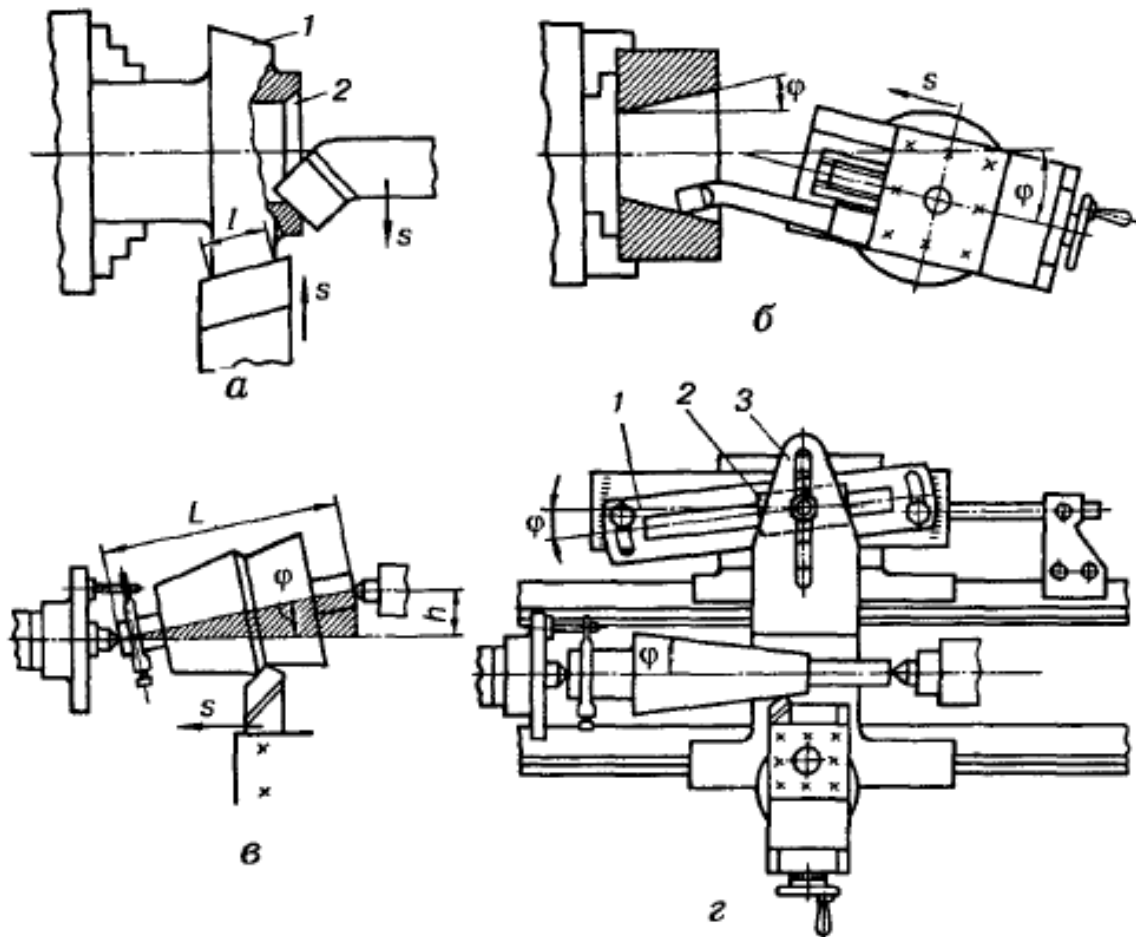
Обробка конічних поверхонь на токарному верстаті
